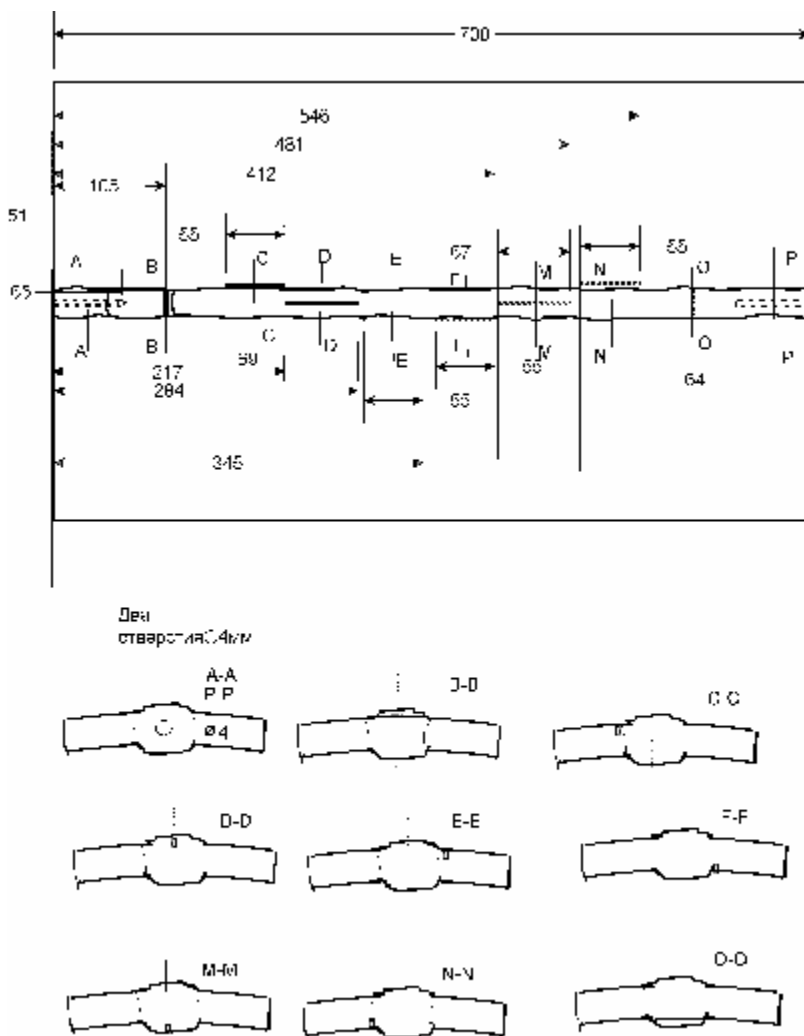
Сварной образец № 1 с моделями дефектов.
